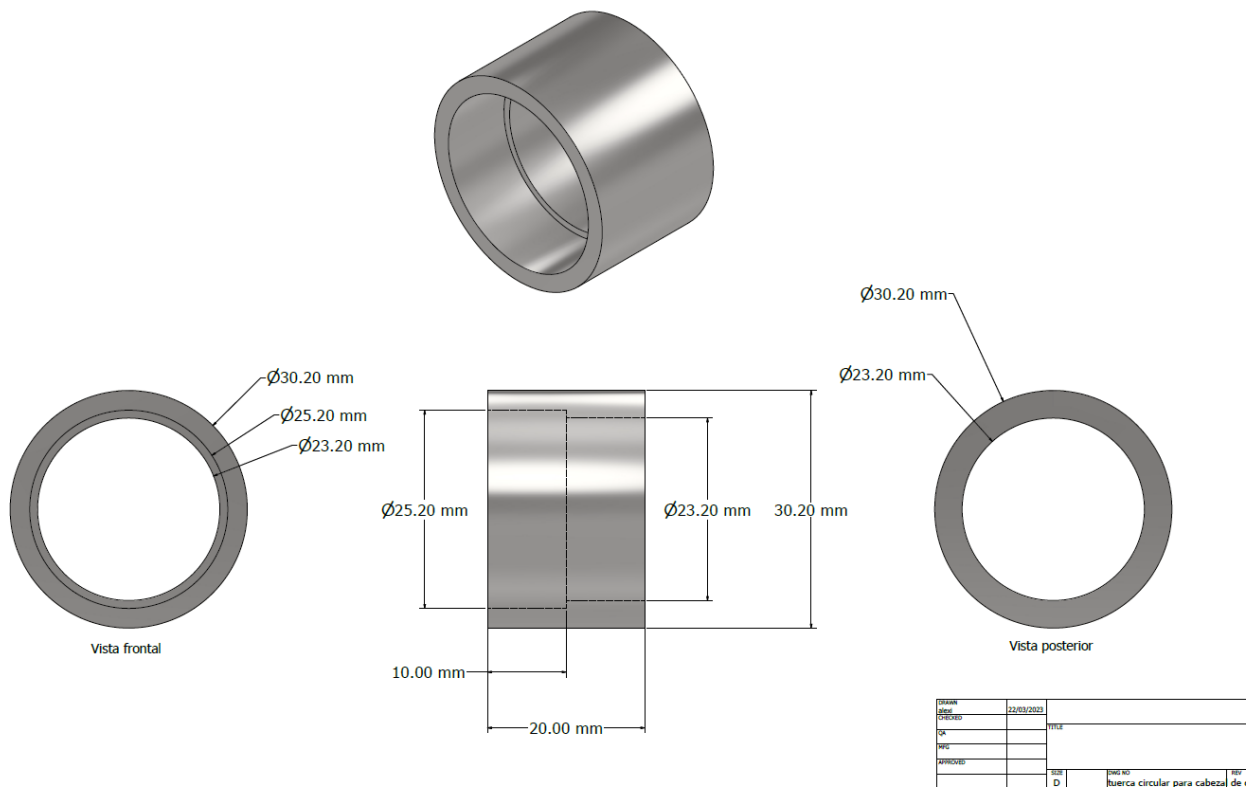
Pieza "B2" de acero que ensambla con pieza "A2".
